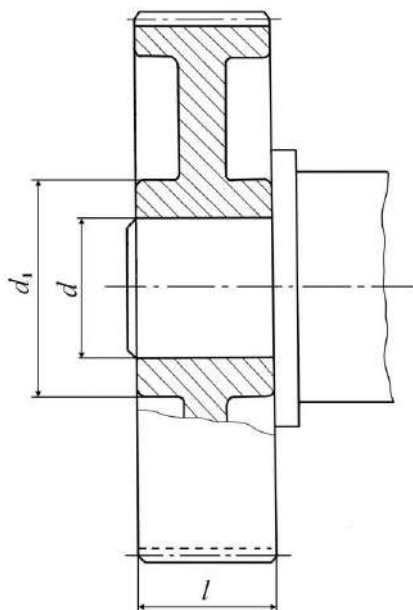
Расчетная схема напрессовки шестерни на распределвал
